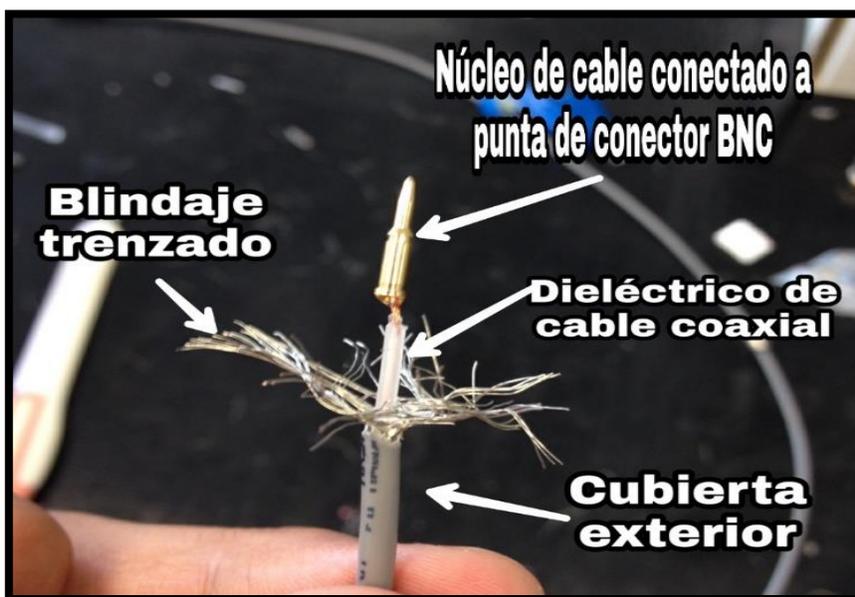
Partes de cable coaxial del electrodo alternativo preparadas para conexión a conector BNC
